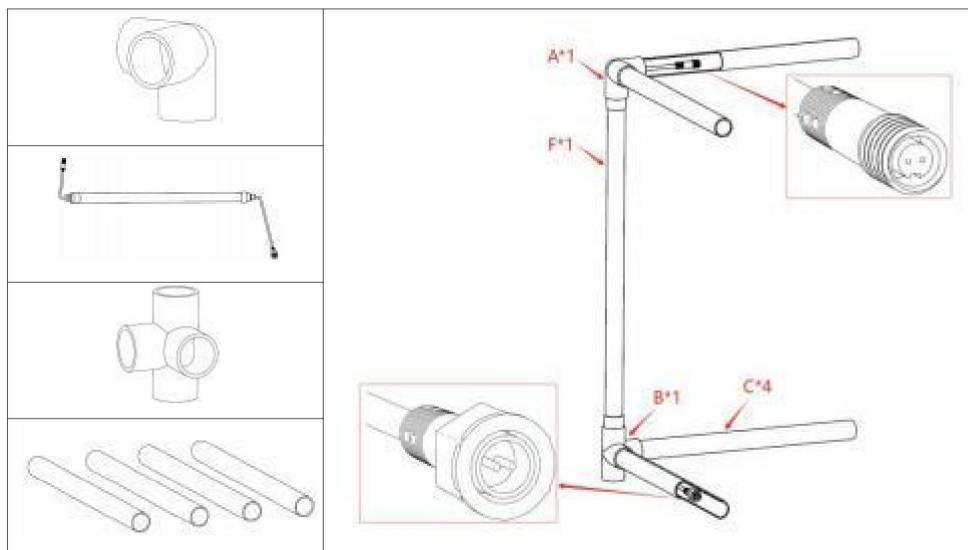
In base alla figura, assemblare quattro tubi trasversali lunghi 355 mm, uno a 4 passaggi, uno a 3 passaggi e una lampada insieme per il backup (Nota: il filo della lampada si trova nel foro di uscita dei tubi a 3 passaggi e a 4 passaggi).
